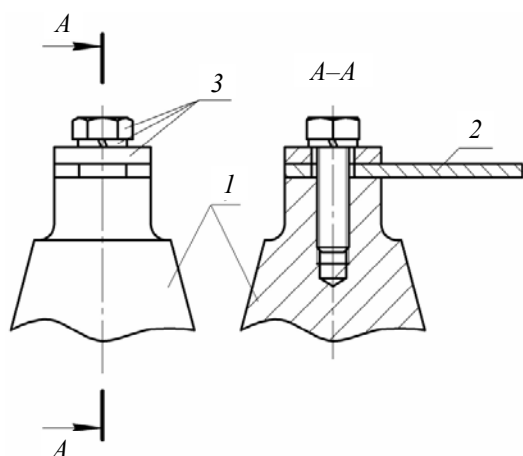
Устройство крепления образца винтом с прижимной планкой:
